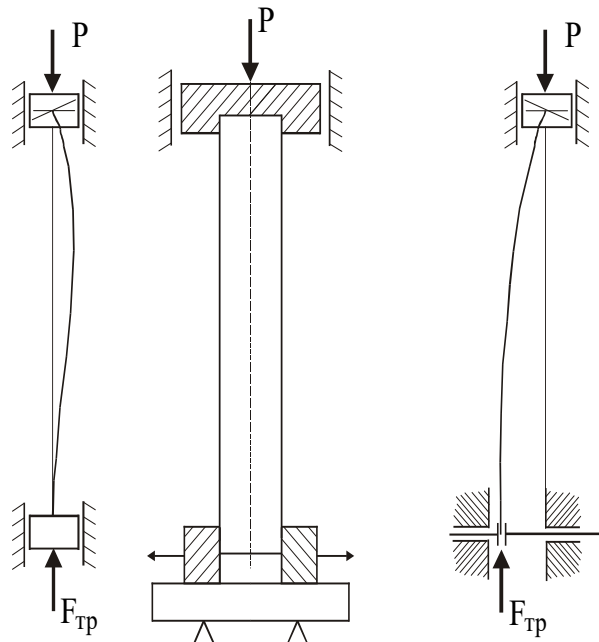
Способ установки и закрепления деталей при запрессовке (свободный конец вала допускает угловые повороты, втулка может горизонтально перемещаться): 1 – стол; 2 – втулка; 3 – вал; 4 – пуансон прессы; 5 – закрепительная втулка
